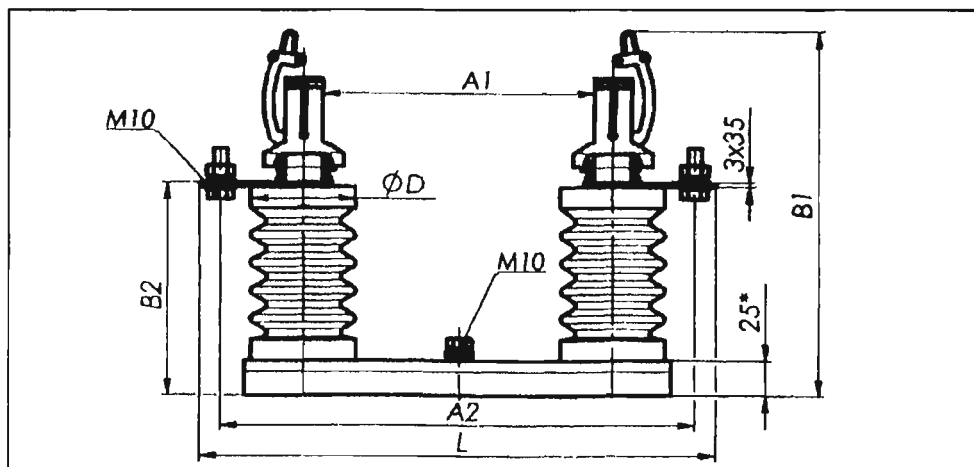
Габаритные и установочные размеры основания высоковольтного предохранителя серии ПКТ- VV
